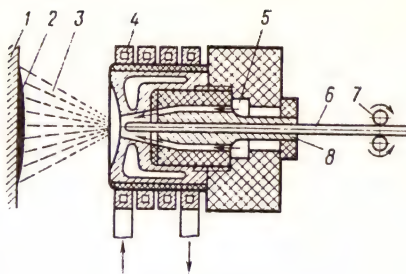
Схема высокочастотного напыления: 1 — напыляемая поверхность; 2 — газометаллическая струя; 3 — концентратор тока; 4 — индуктор, охлаждаемый водой; 5 — воздушный канал; 6 — проволока; 7 — подающие ролики; 8 — направляющая втулка
